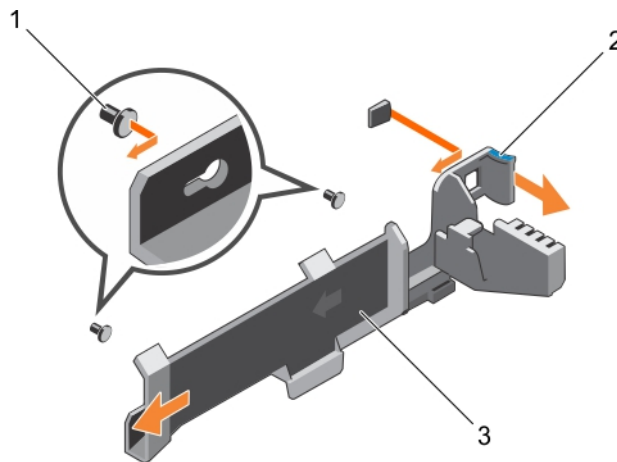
Rimozione e installazione della staffa di contenimento del cavo
